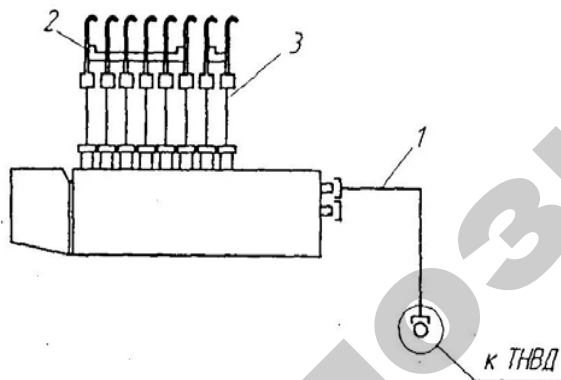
Схема соединения топливопроводов при испытании ТНВД методом пролива:
